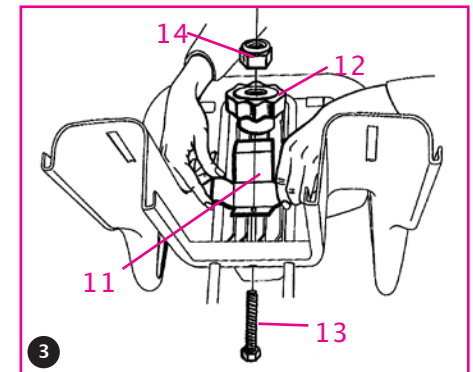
Schließlich die selbstsichernde Mutter (14) einschrauben.
